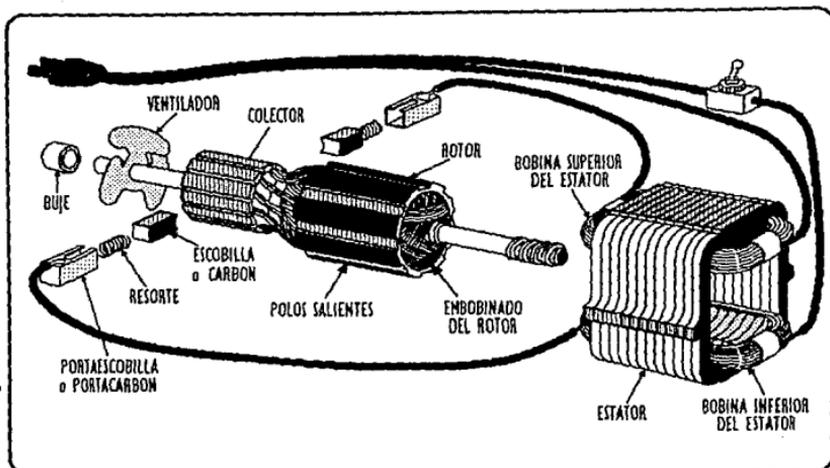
DESPIECE REPRESENTATIVO DE UN MOTOR UNIVERSAL.
